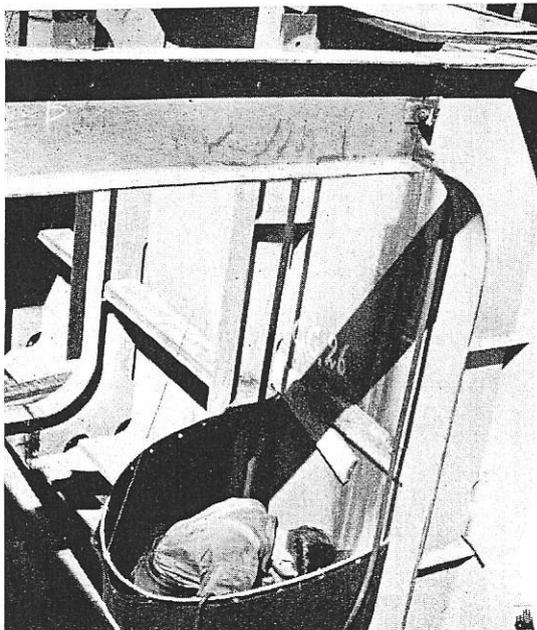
Exécution d'une soudure à une maîtresse poutre. On note les bâches protégeant le soudeur.
